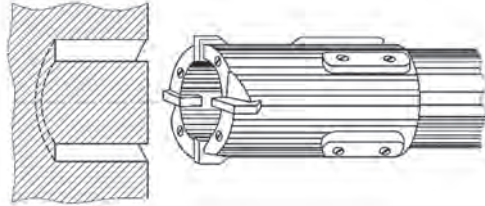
Схема обробки свердлом для кільцевого свердління
